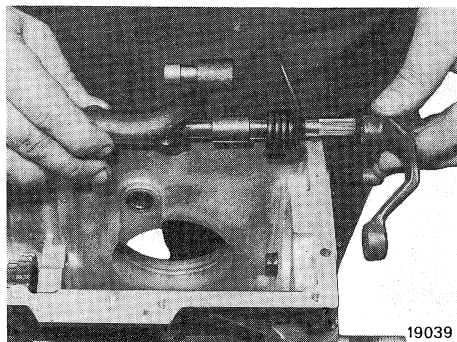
Ilustra las piezas componentes del tornillo sin fin en la versión sin inversor.
